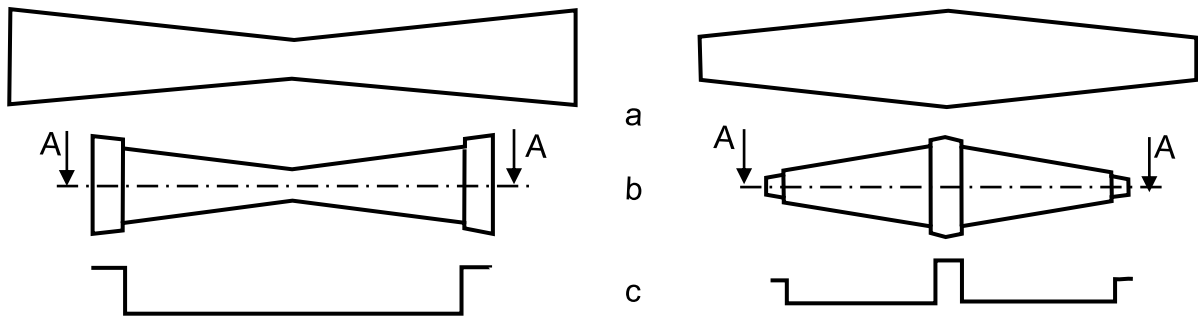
Prinzipskizzen zur Gestaltung der Klauenpolbleche: a) Ausgeschnittene Bleche, b) Draufsicht auf die Polbleche nach dem Biegeprozess, c) Biegelinie: Schnitt A-A
